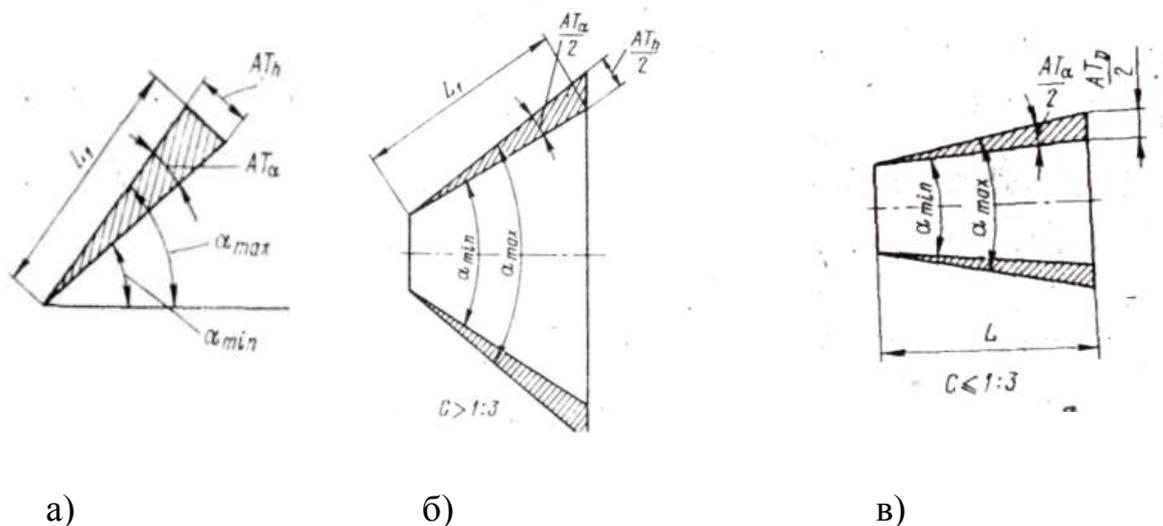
Допуски угловых размеров и их обозначения
